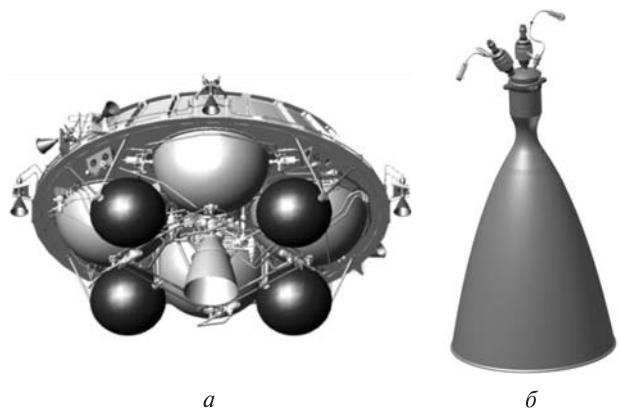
Двигательная установка ДУ802 (а) и апогейный двигатель РД840 (б)
